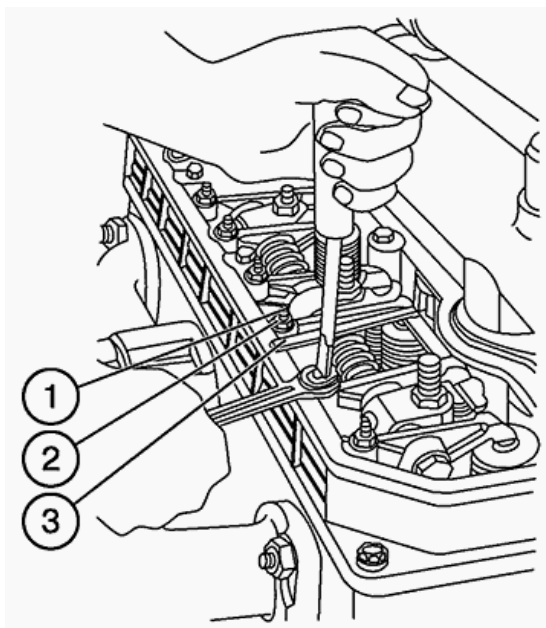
Регулировка зазоров в клапанах двигателя Д-243
